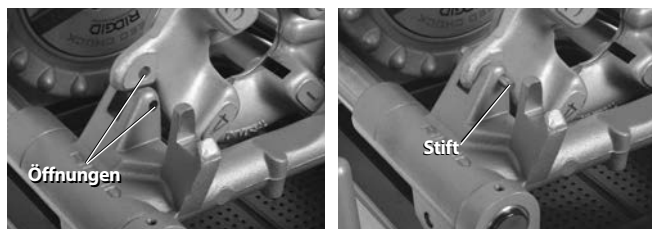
Halten des Linksgewindeschneidkopfs
